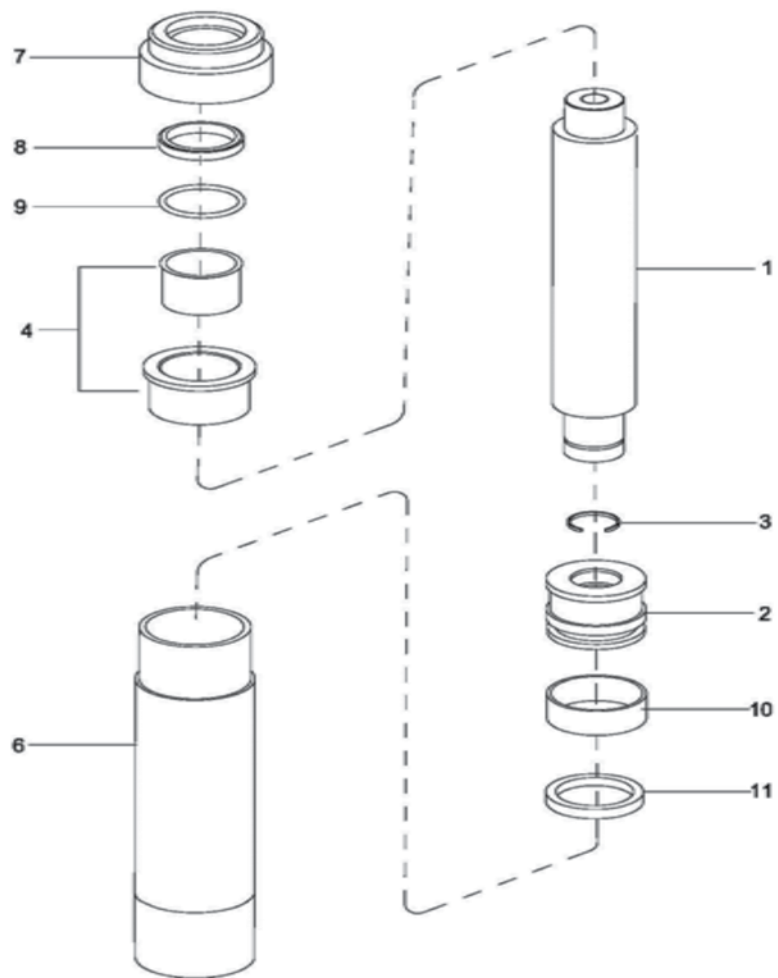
ASSEMBLAGE POMPE ET MOTEUR
